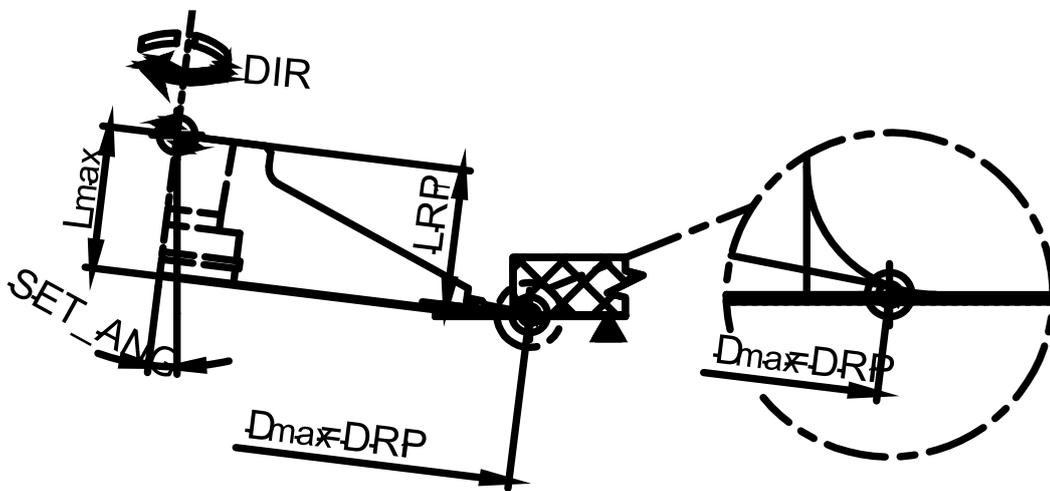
Maßdefinition für Postforming-Werkzeuge (Beispiel Fasefräser)
